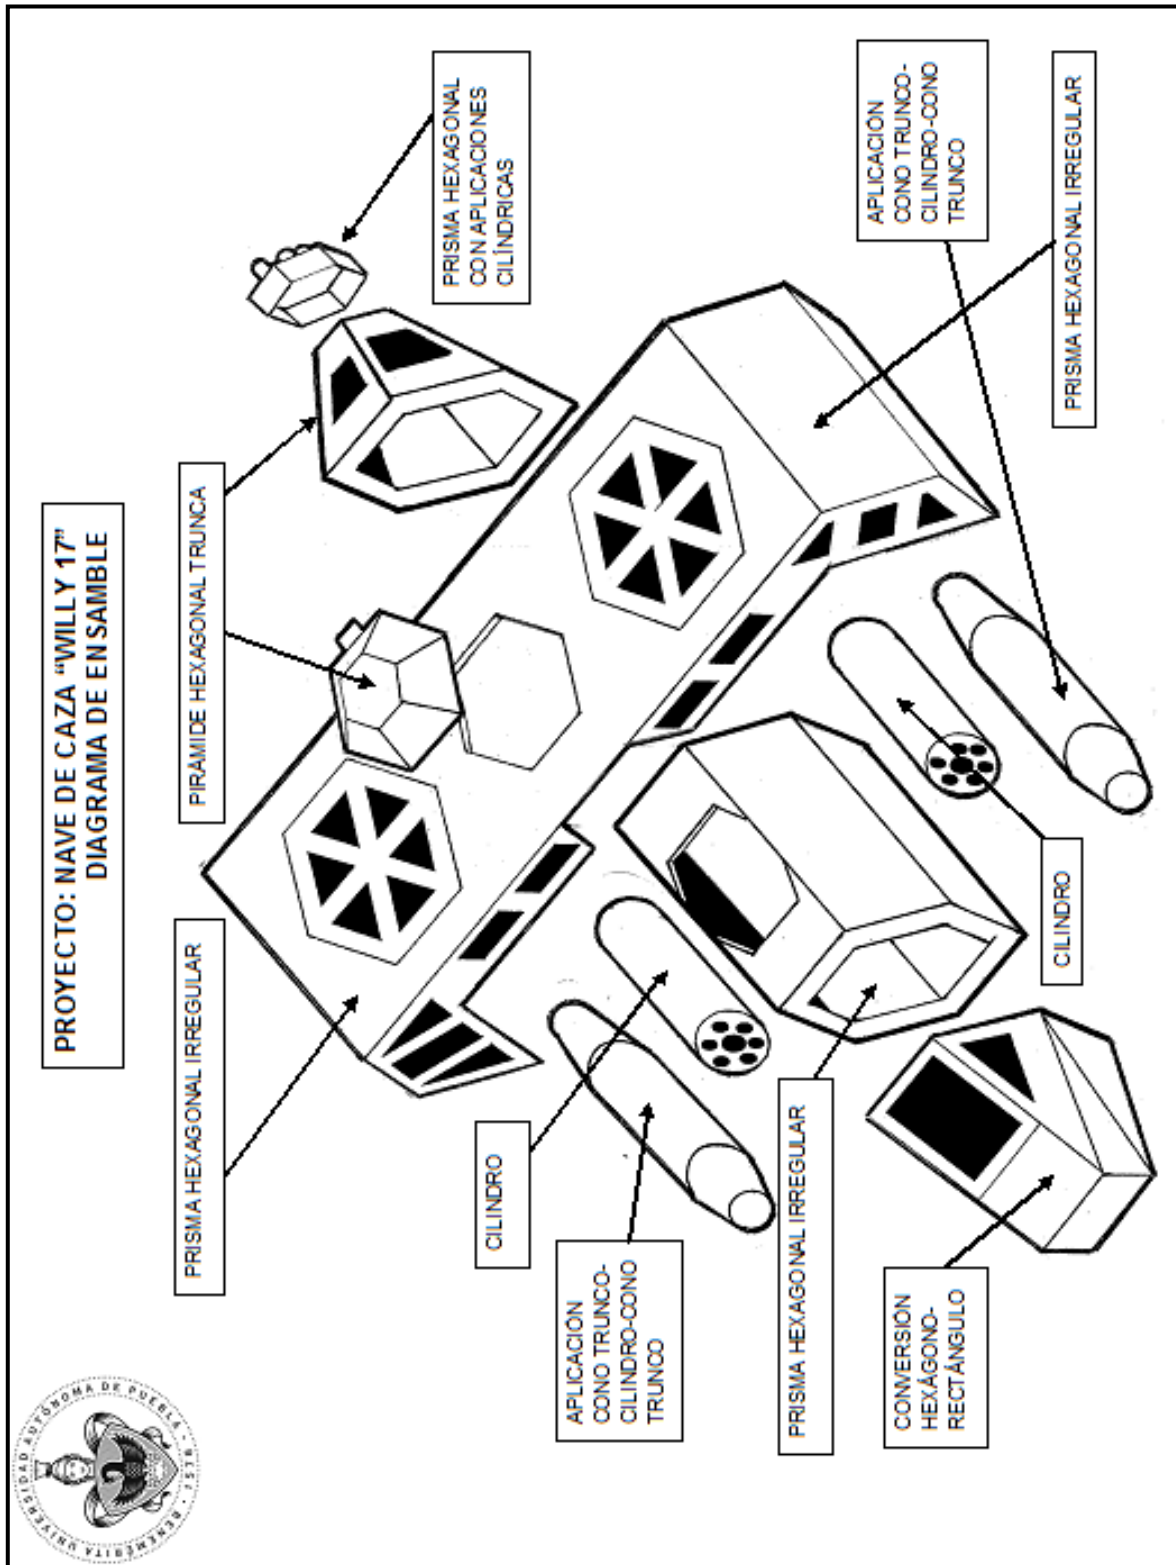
Práctica 52 Willy 17, vista explosionada
